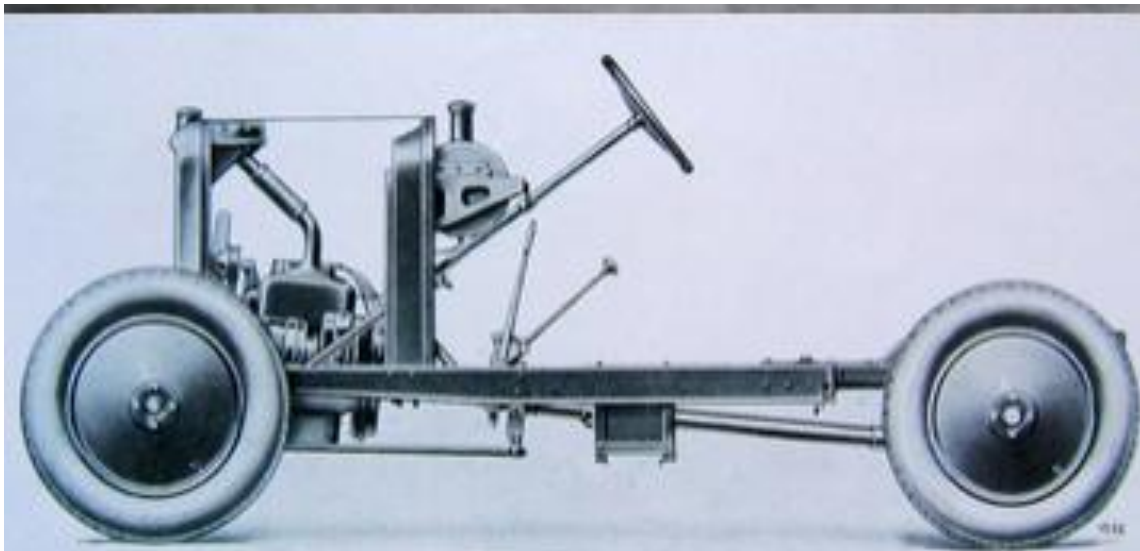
VUE EN ÉLEVATION DU CHASSIS 5 CH, TYPE 172-M 2.
